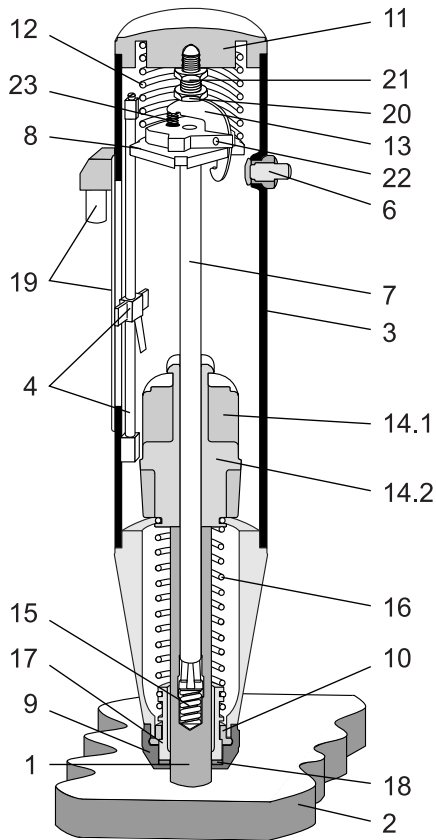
Längsschnitt durch Betonprüfhammer
